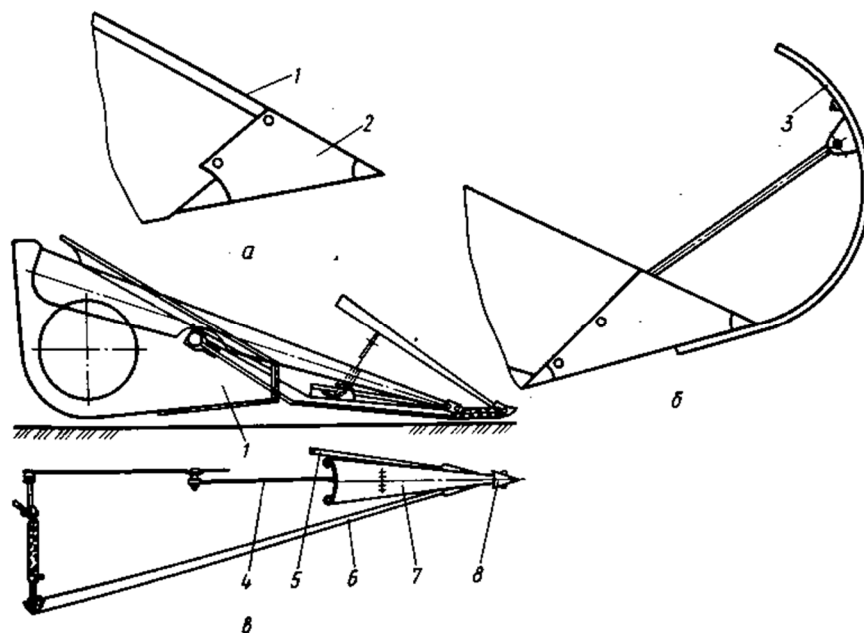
Схемы пассивных делителей: а – клиновой; б – прутковый; в – торпедный; 1 – боковина жатки; 2 – носок клинового делителя; 3 – пруток делителя; 4 – тяга; 5 и 6 – внутренний и наружный стеблеотводы; 7 – корпус; 8 – носок корпуса.
